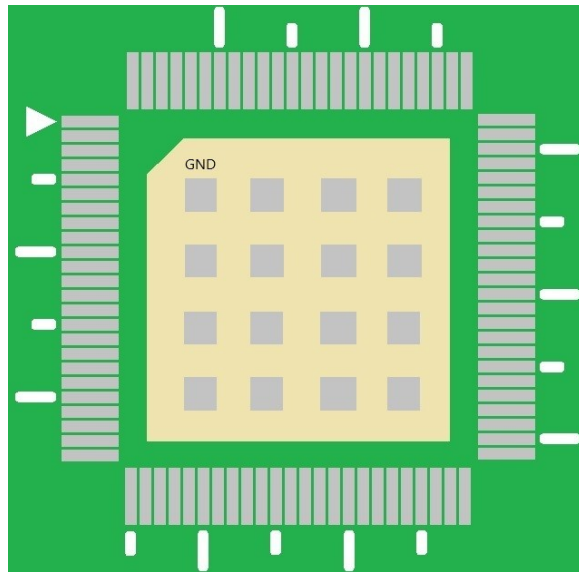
：LT7589A 底部焊盘 PCB 的设计建议-1
